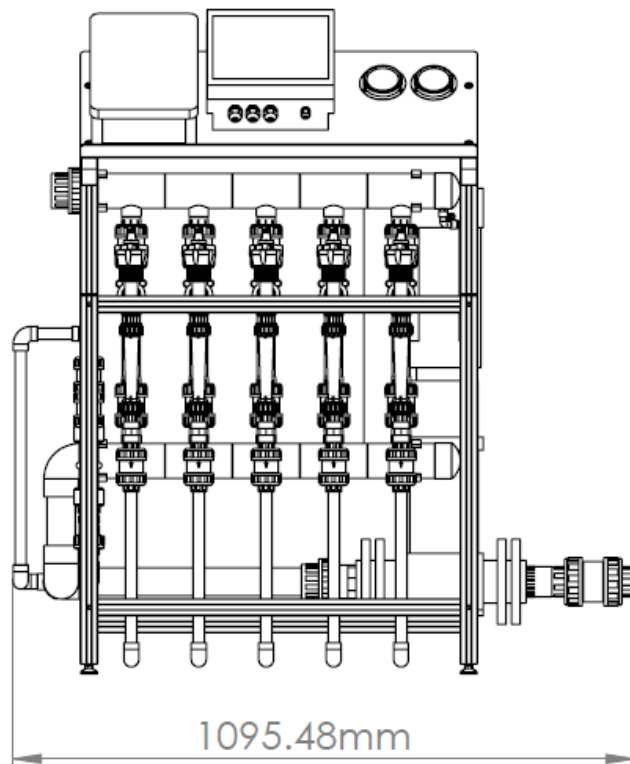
Dibujo de la parte frontal de la máquina del prototipo número 1 en el plano de dimensiones.
